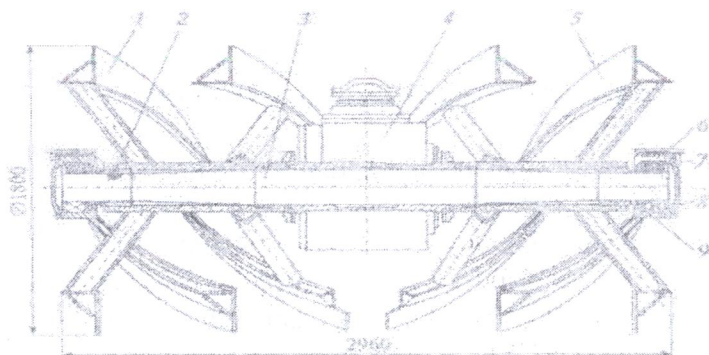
Фреза: 1 и 5 – ленточные шнеки; 2 – штифт; 3 – ось; 4 – конический редуктор; 6 – рама рабочего органа; 7 – подшипник; 8 – крышка; 9 – корпус
